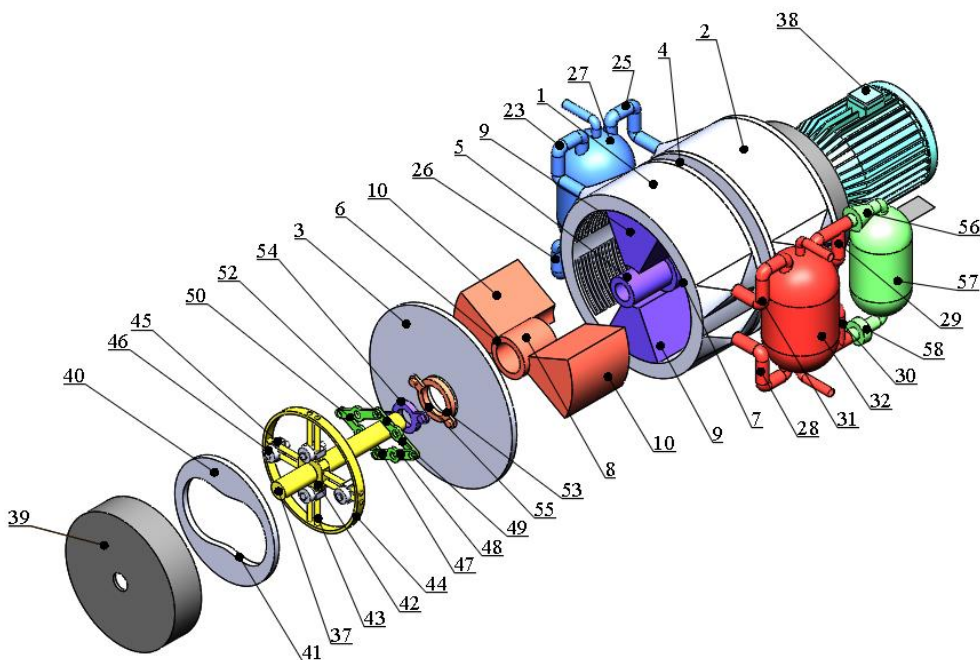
РЛГХМ з рознесеними деталями конструкції
